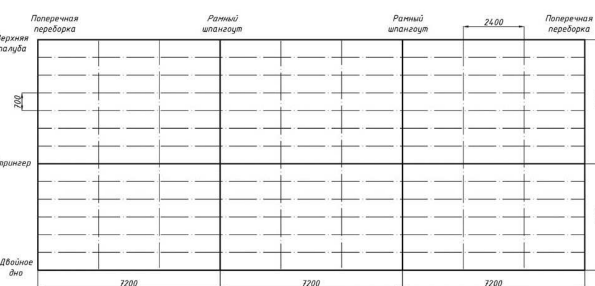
Расчетная схема набора бортового перекрытия, набранного по продольной системе набора с диагональными элементами
